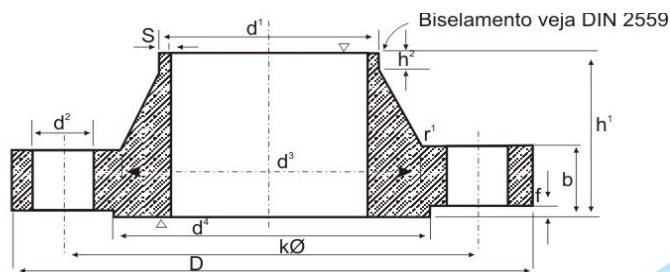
D16 - FLANGE COM PESCOÇO (DIN)
